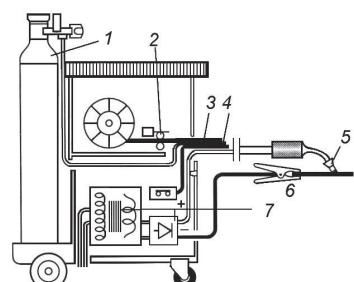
Установка для напівавтоматичного зварювання в захисному газі:
